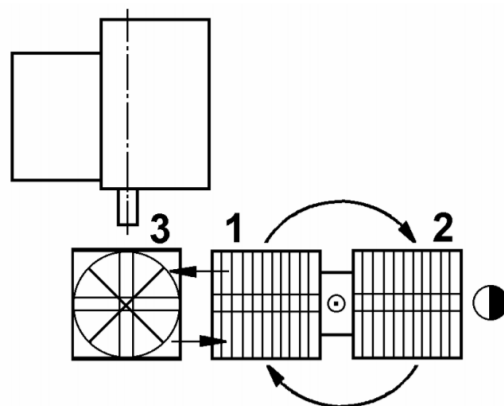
Systém automatickej výmeny obrobku s dvomi paletami [12]
